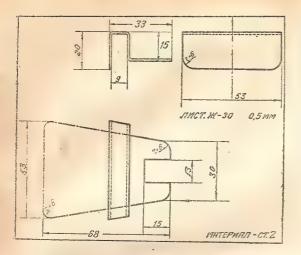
Пружина неподвижной стойки автомата для смены пластинок
